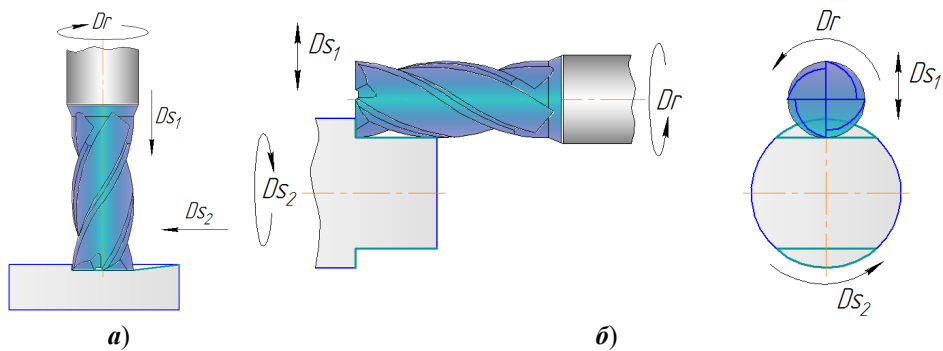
Схемы обработки с врезанием фрезы по касательной: *a* – плоской поверхности детали; *б* – плоской и цилиндрической поверхностями детали
